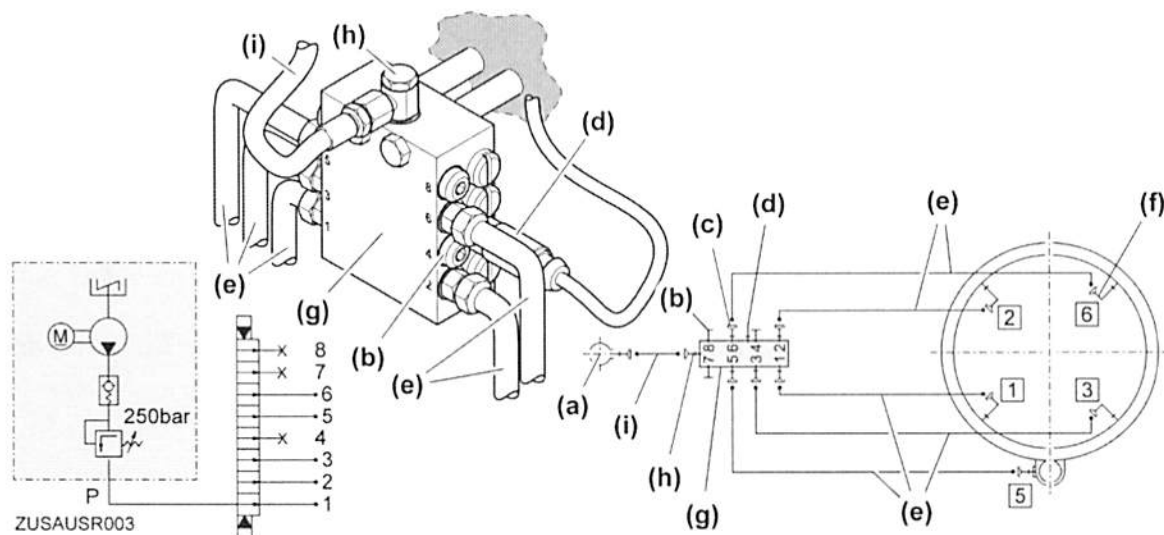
Verlegeplan und Hydraulik-Schaltplan (8er-Verteiler mit einem Drehwerk)
